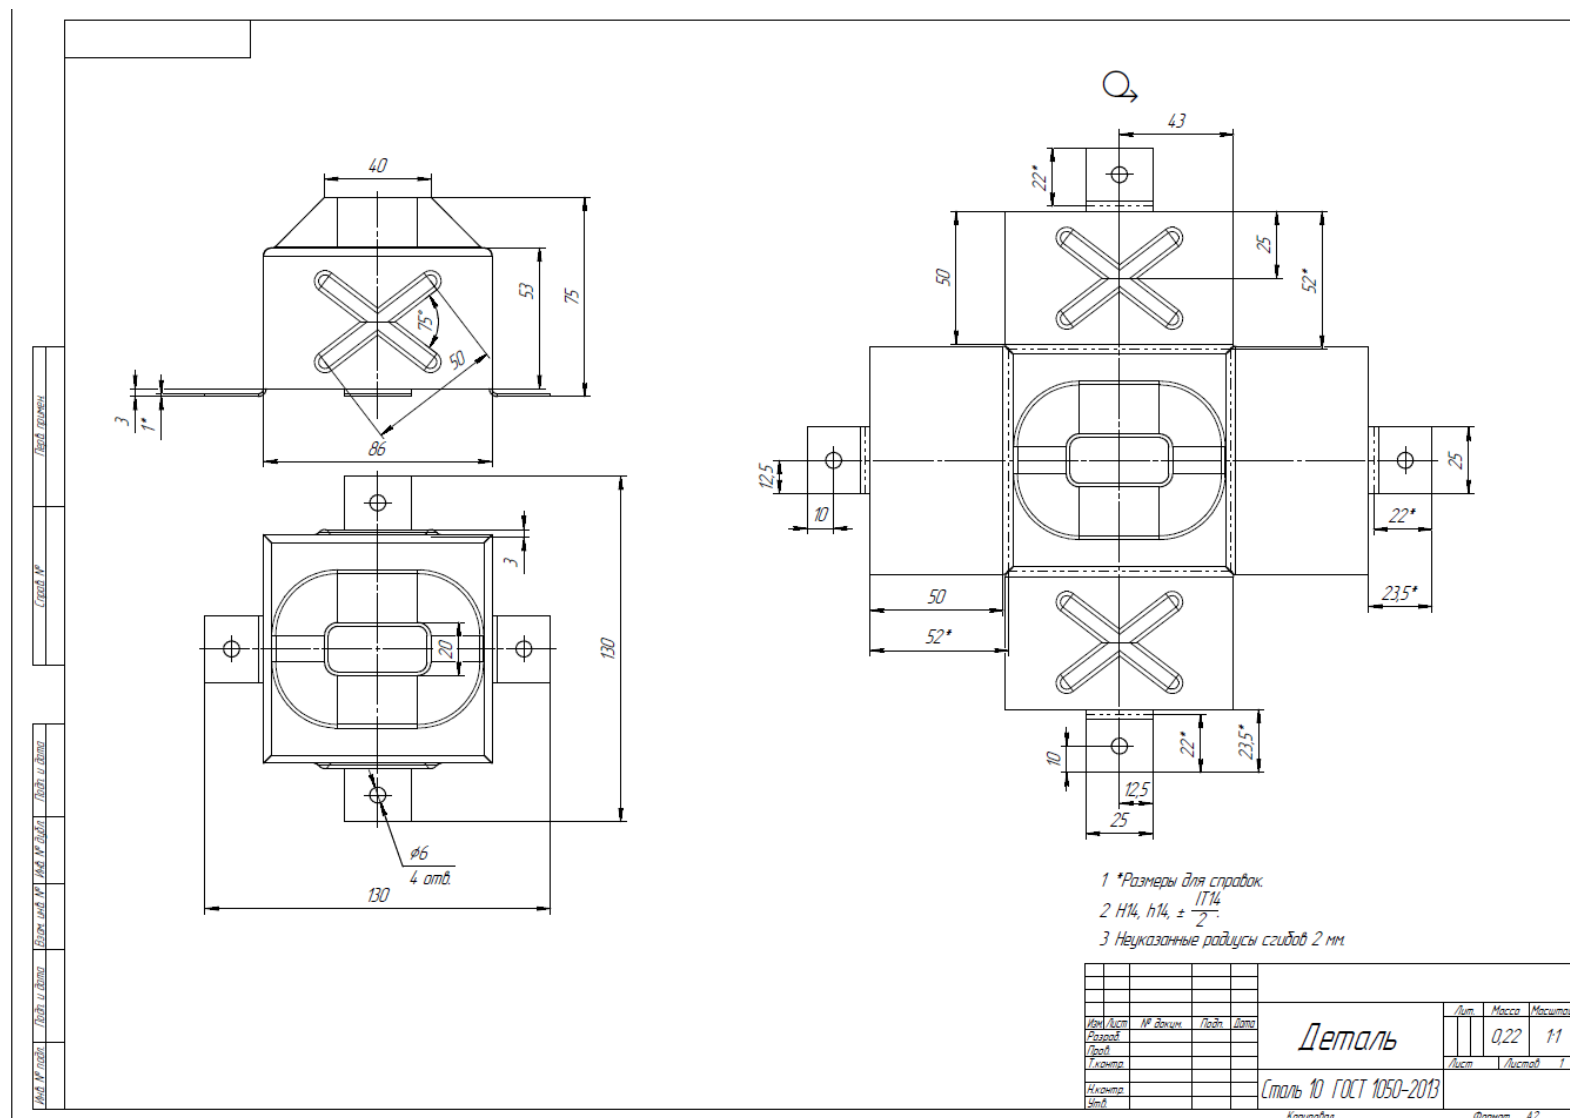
Чертеж детали «Корпус» (вариант 3)
